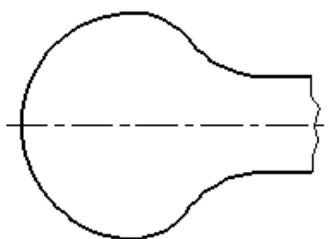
Образец оформления плавного перехода от одной поверхности к другой
